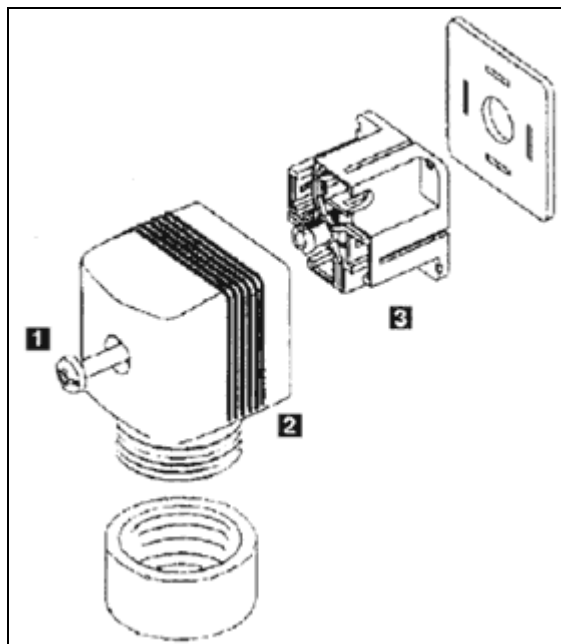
Кабельный разъем тип 2508 стандарта DIN 43 650 A
